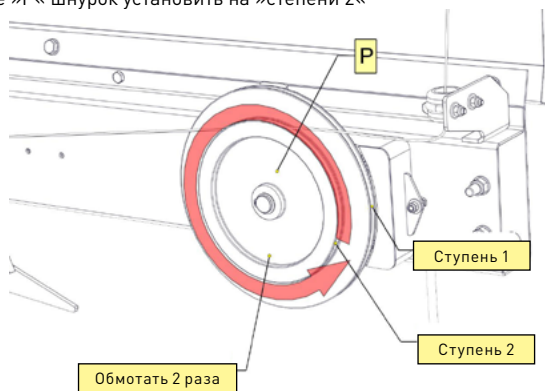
Регулировка плотности обмотки рулона шпагатом.
